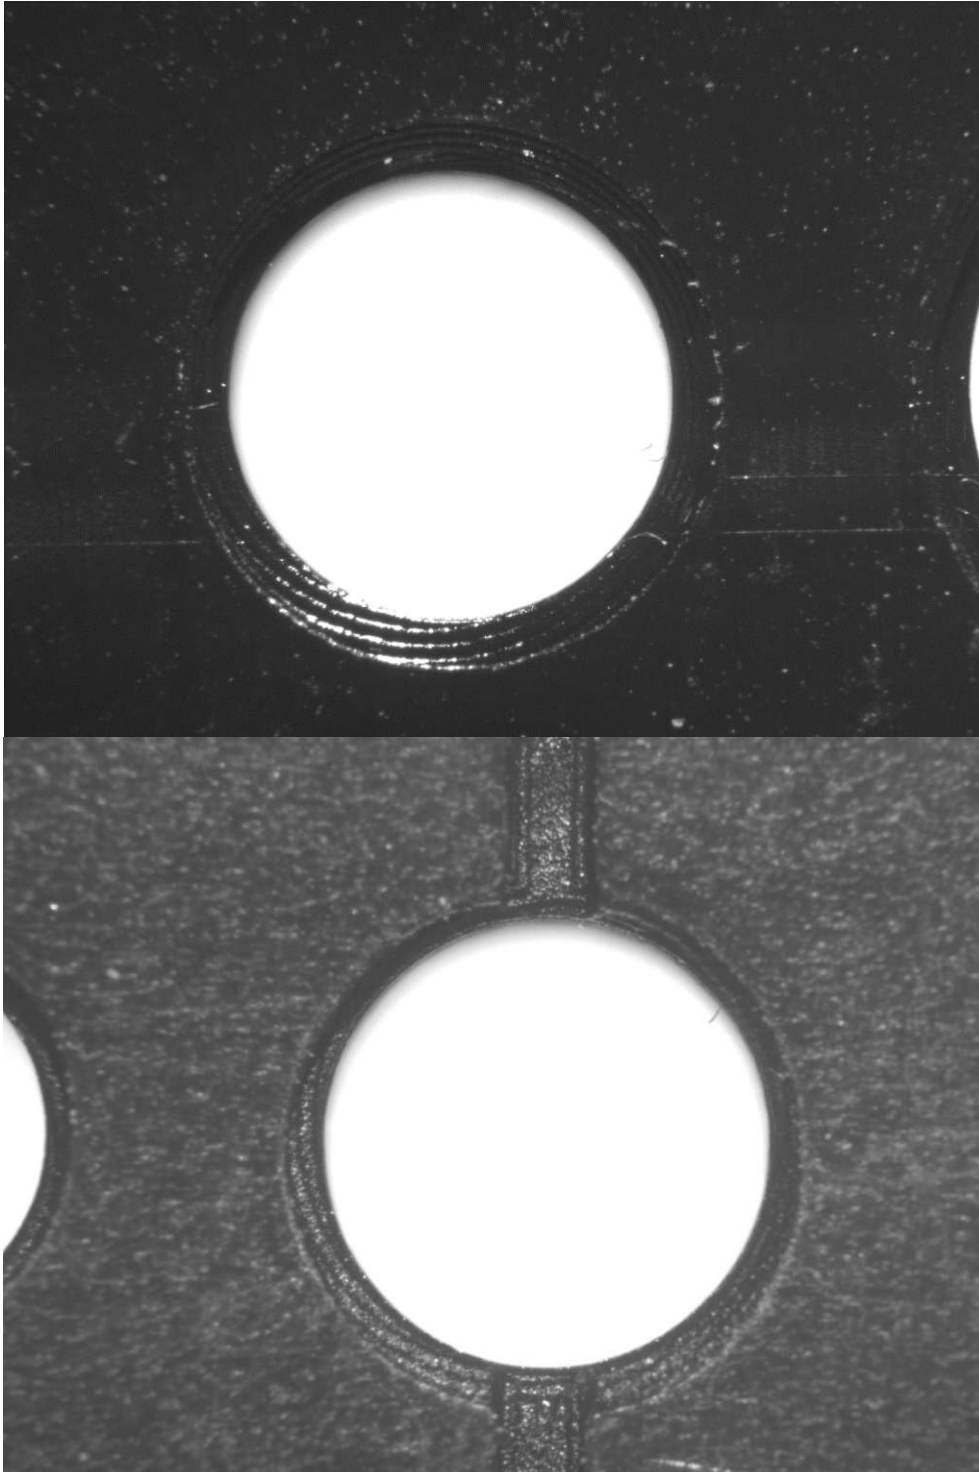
M6 Gewinde in Z gedruckt. Drauf und Rückansicht
